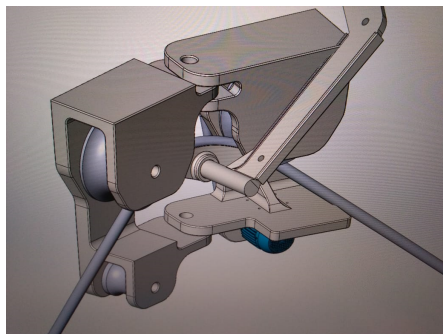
Базовый макет шарнирно-сочлененной каретки
